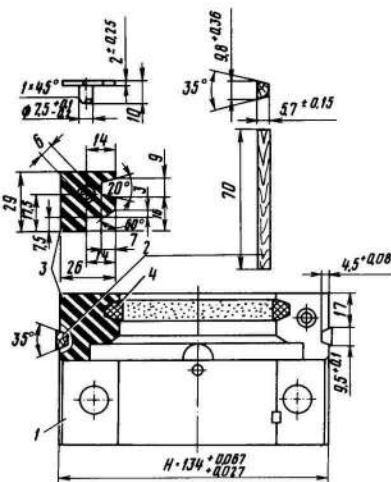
Уплотнение заднего коренного подшипника в крышке:
